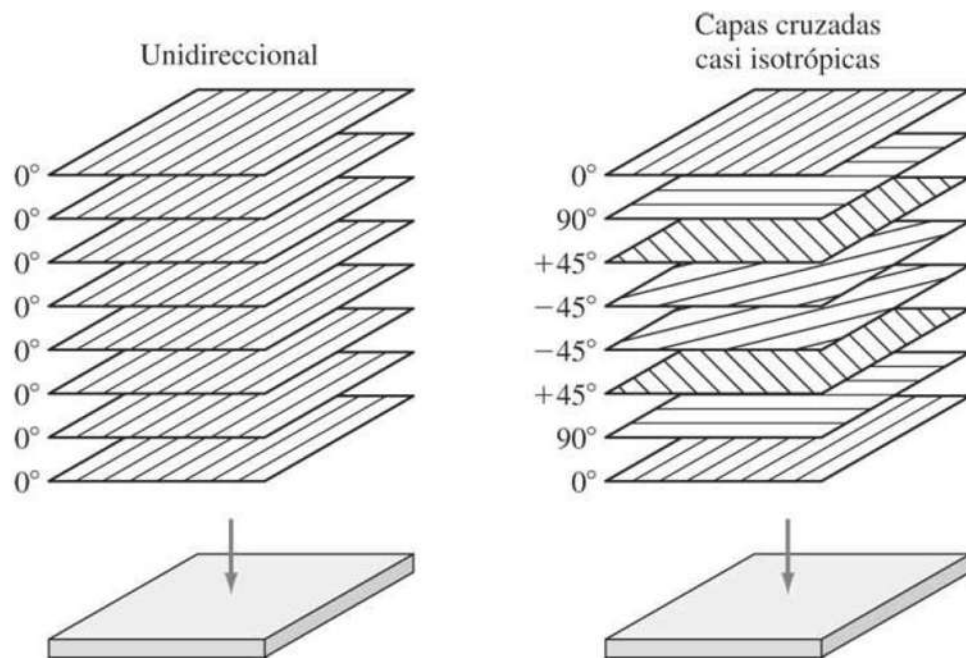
Capas de laminado unidireccional y capas de laminado bidireccional. [31]
